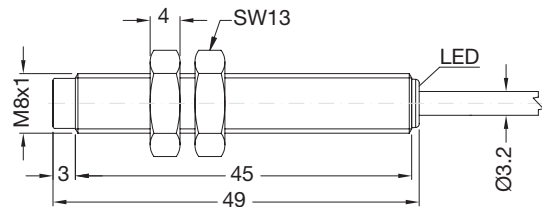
Lange Ausführung, Nicht bündiger Einbau, Kabel
